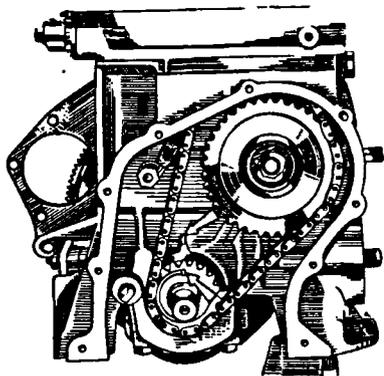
Проверка совпадения установочной метки на звездочке коленчатого вала с меткой на блоке цилиндров
